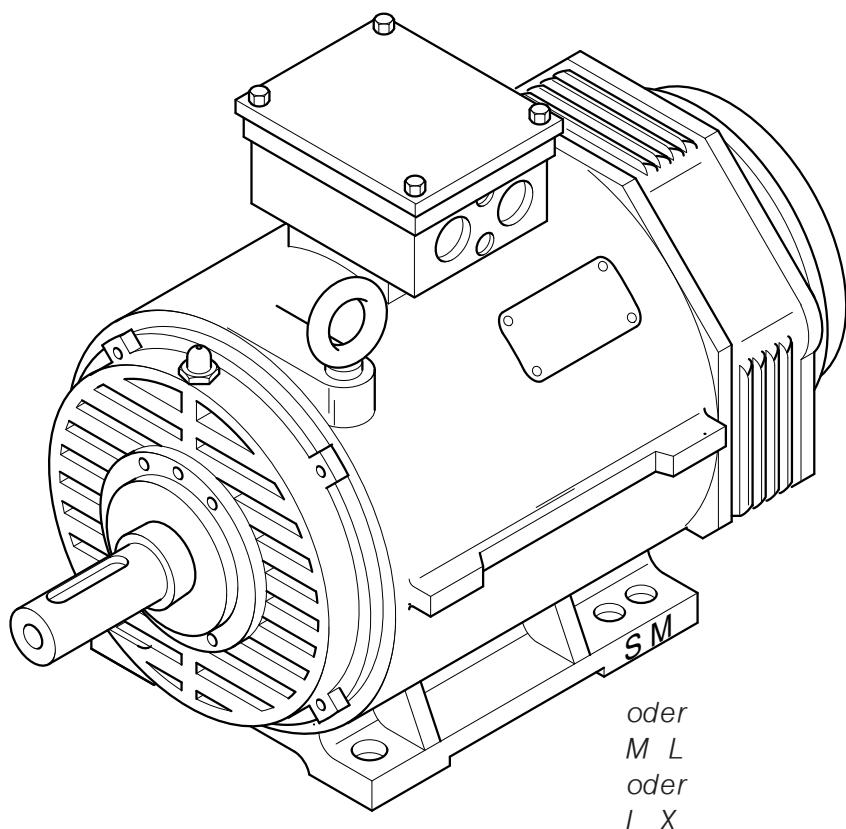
Отверстия для опорного крепления S,M или M,L или L,X
